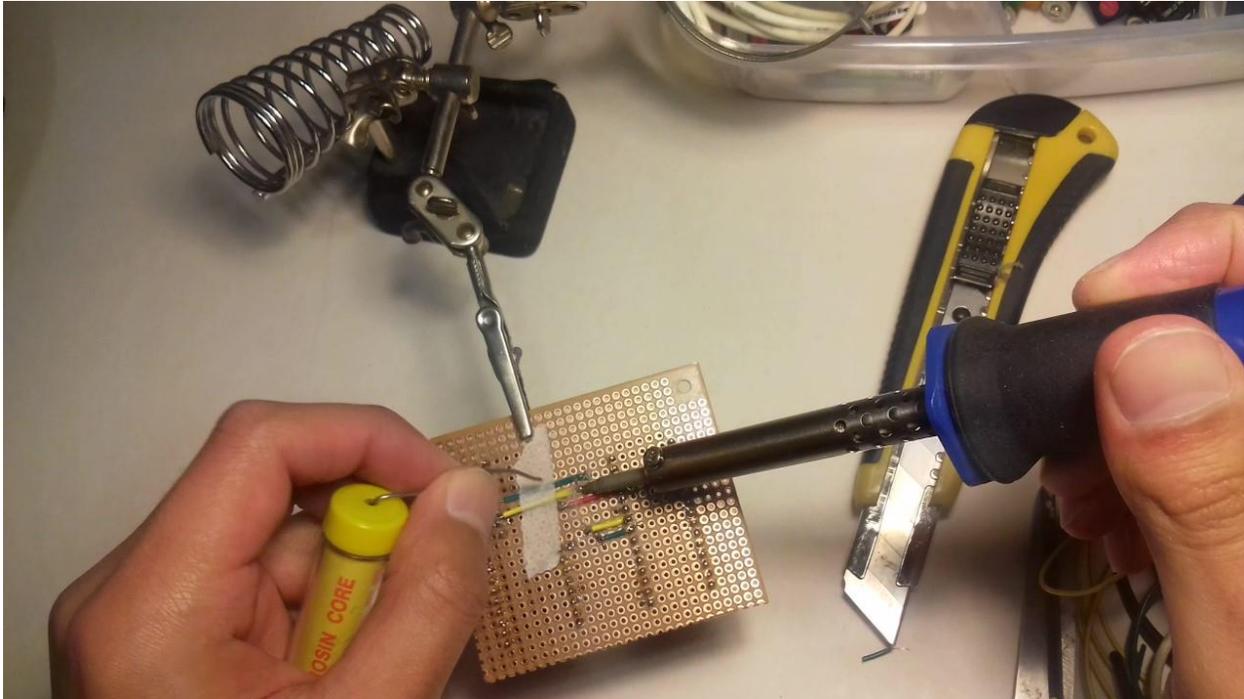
Placa PCB perforada siendo soldada por el lado inverso. En la imagen se puede ver la integración de los cables entre las distintas conexiones dentro de la placa.
